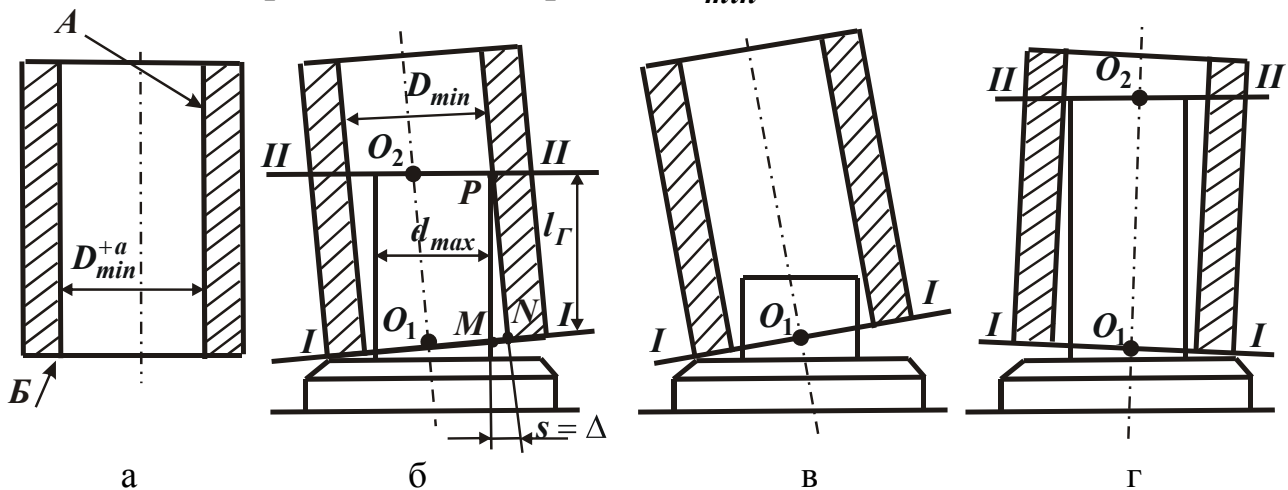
Базирование заготовки на пальцы различной длины.
